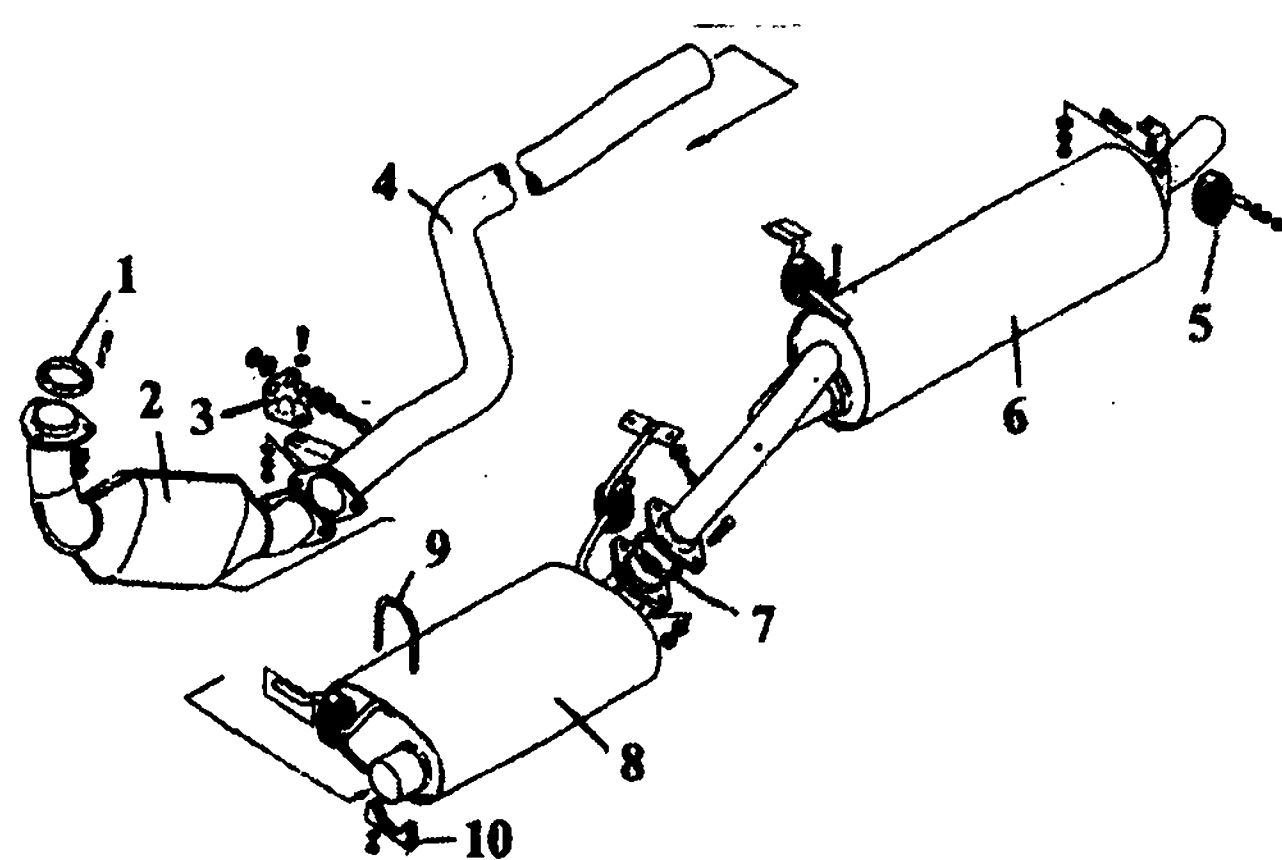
Система выпуска газов: 1 - прокладка; 2 - нейтрализатор; 3 - кронштейн; 4 - промежуточная труба; 5 - амортизатор; 6 - глушитель; 7 - прокладка; 8 - хомут; 9 - резонатор; 10 - стремянка
